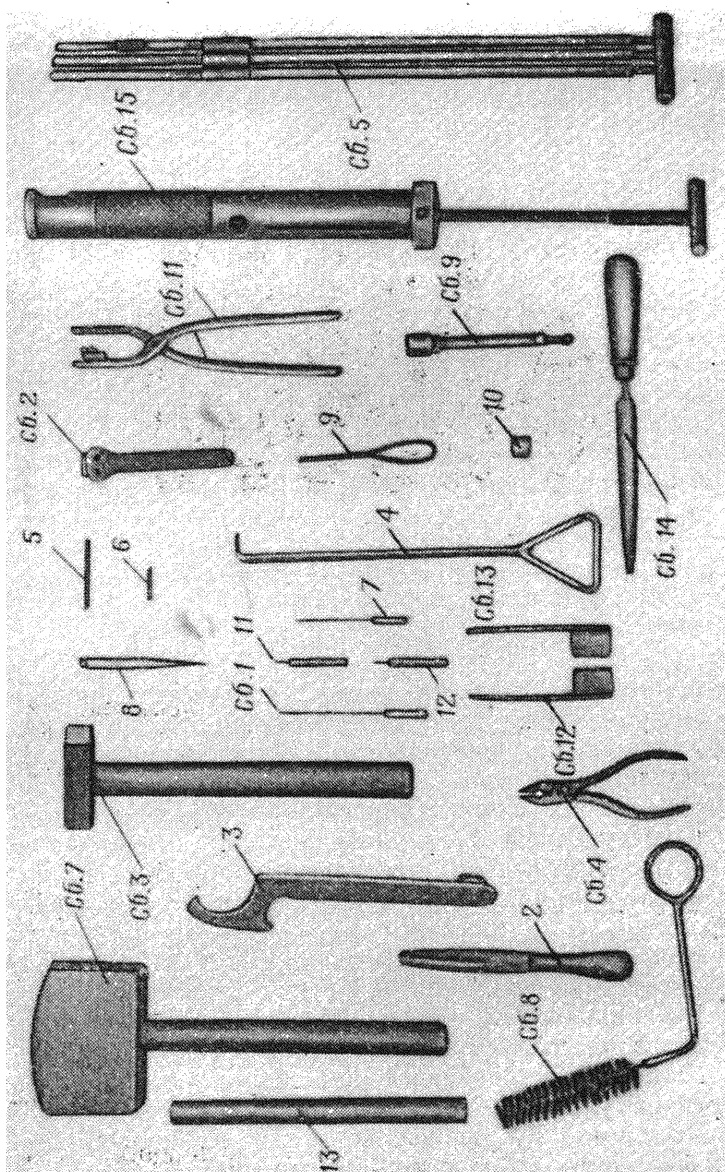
Инструмент и принадлежность (позиции обозначают номера деталей):
